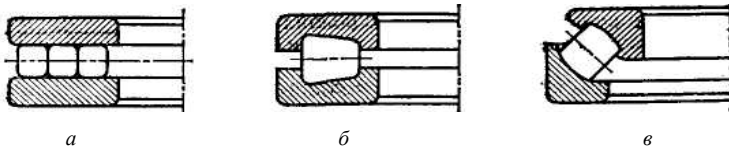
Роликоподшипники упорные или упорно-радиальные типов:
